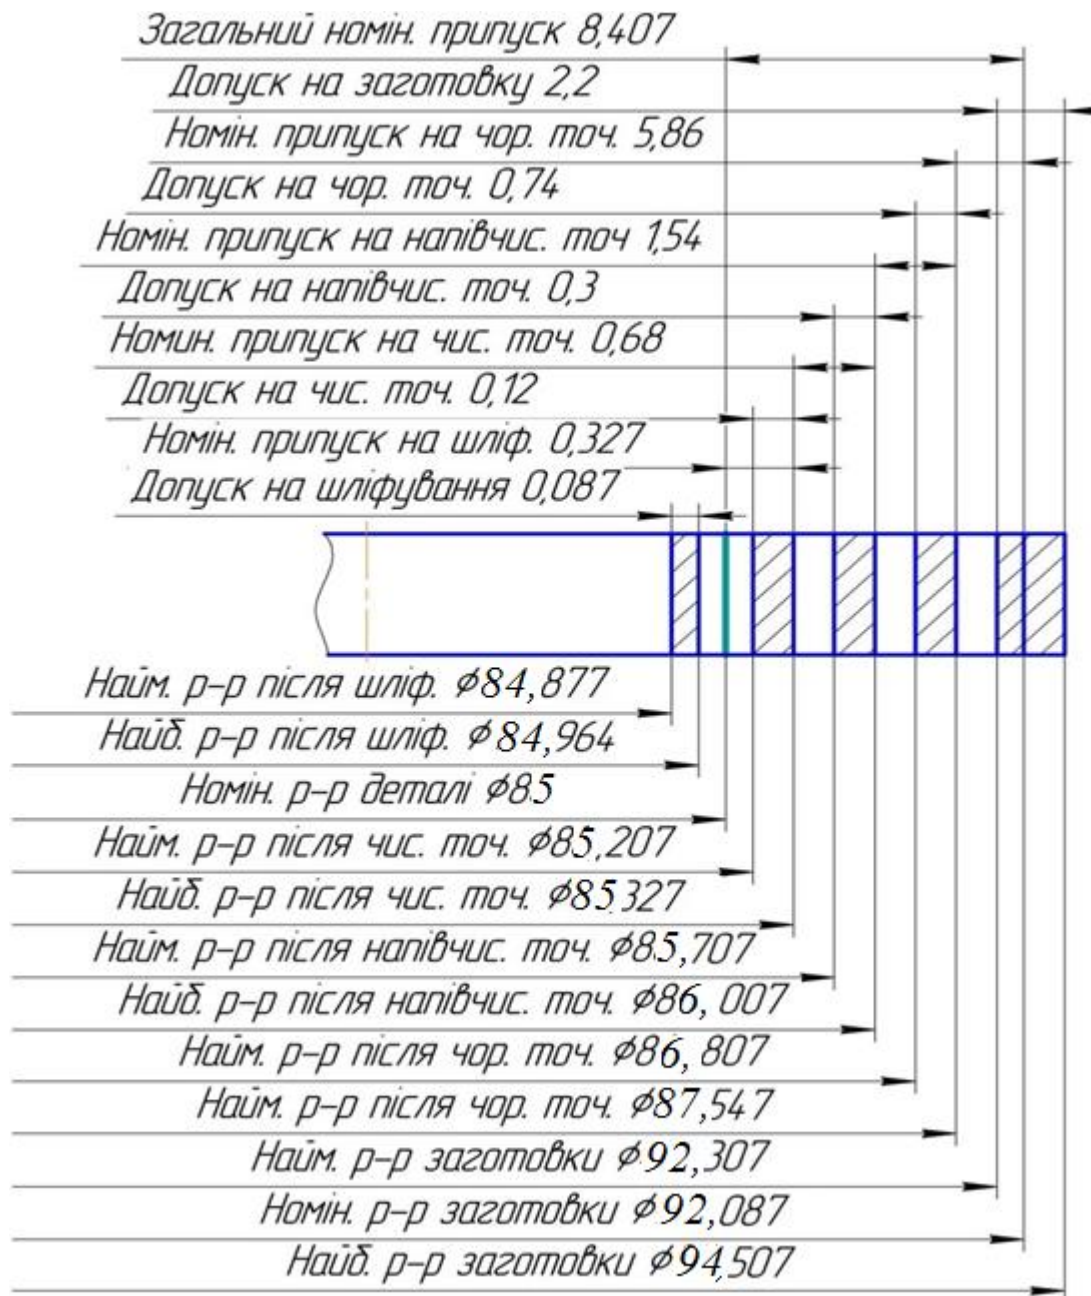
Схема розміщення припусків і допусків на оброблення початкової заготовки для отримання поверхні $\phi 85f9$
